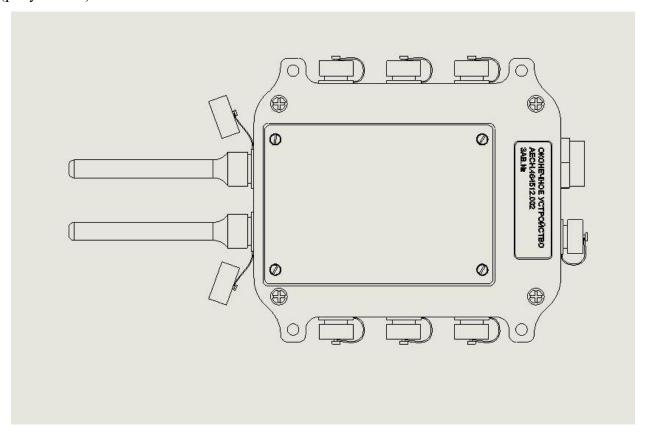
Маркировка ОУ (вид снизу)
